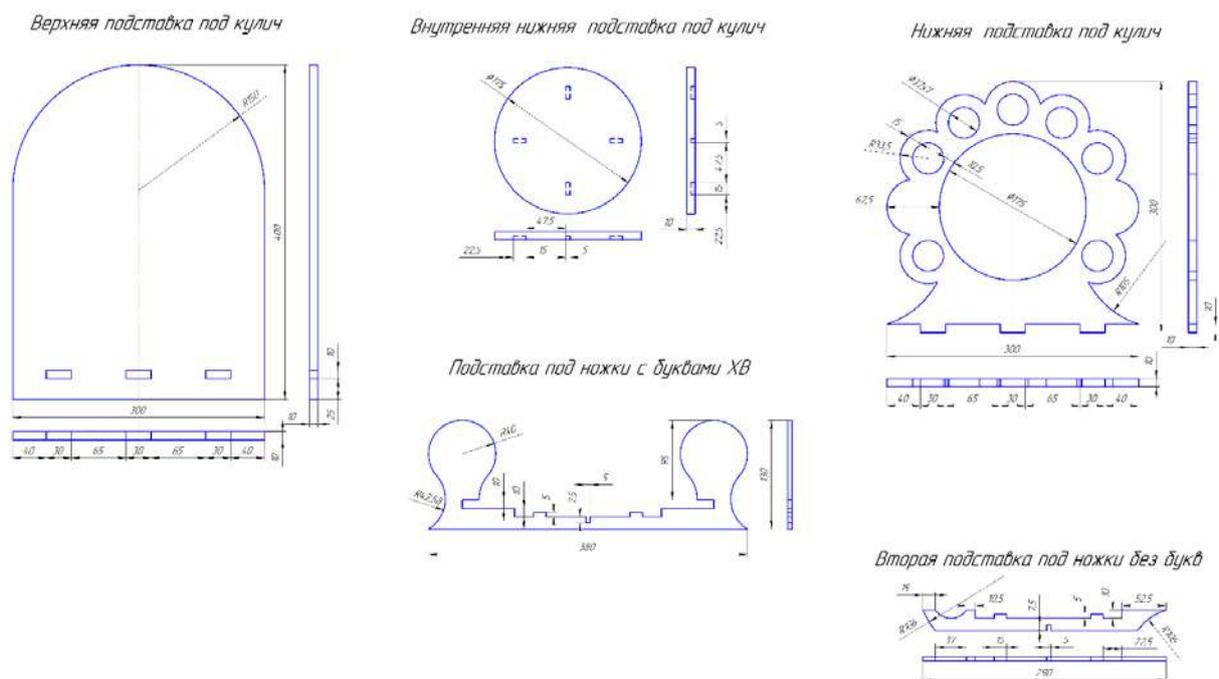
Чертежи необходимых деталей для изделия «Подставка под кулич»
